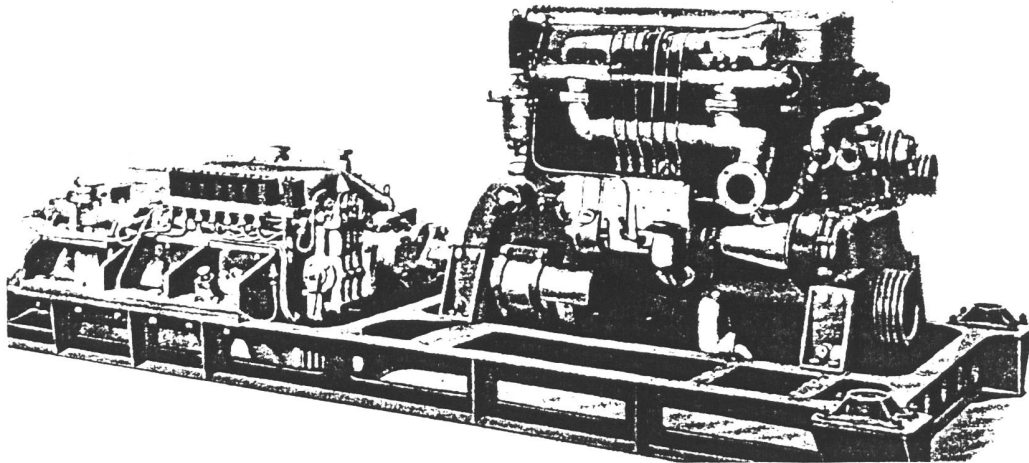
Motor-Getriebe-Aggregat, auf dem sog. Maschinenrahmen montiert (die elektro-pneumatischen Ventile des Stufengetriebes sind normalerweise verschalt)
